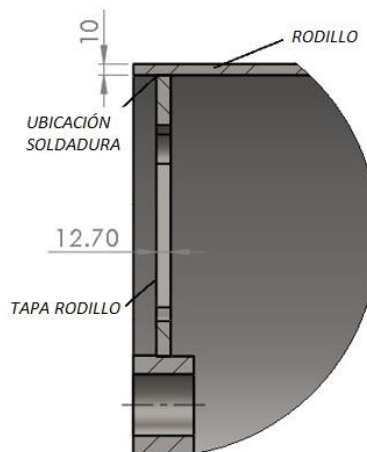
Ubicación soldadura N° 2
